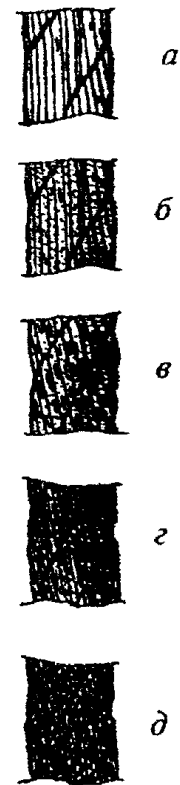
Поверхностная коррозия проволок каната крестовой свивки:
